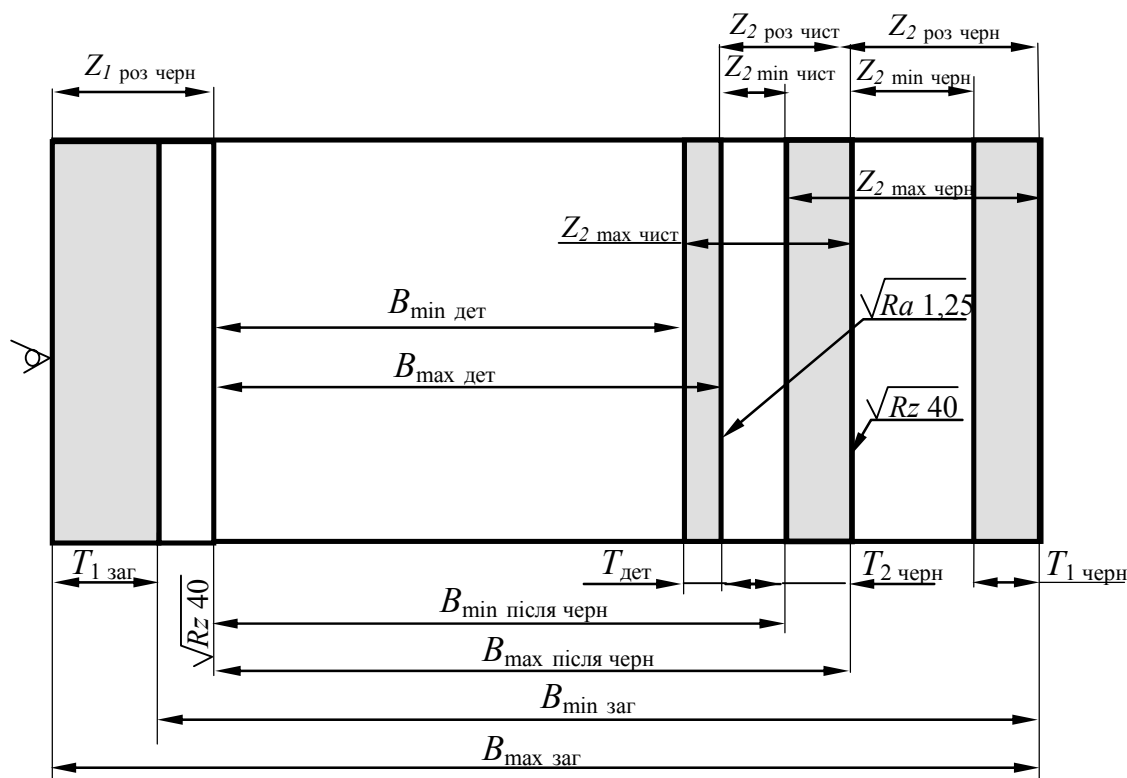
Схема розташування припусків і допусків деталі при фрезеруванні
